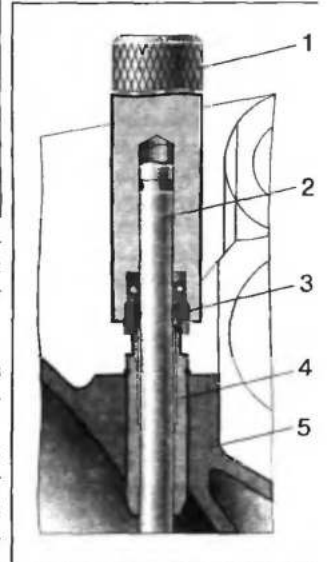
Оправка для запрессовки маслоотражательного колпачка клапана: 1 — оправка; 2 — клапан или направляющий стержень; 3 — маслоотражательный колпачок клапана; 4 — втулка клапана; 5 — головка блока цилиндров
